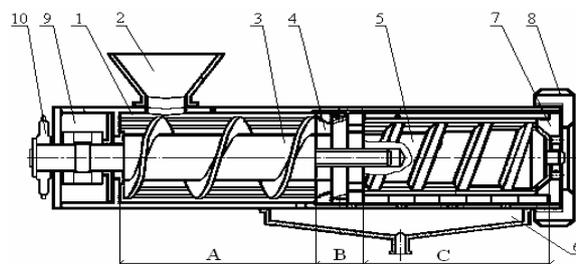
Схема процессов измельчения и прессования мясокостной шквары в экспериментальной установке: А - зона транспортирования, В - зона измельчения, С - зона прессования; 1 - цилиндрический корпус; 2 - бункер; 3 - транспортирующий шнек; 4 - режущий механизм; 5 - прессующий шнек; 6 - поддон для сбора жидкой фракции; 7 - регулируемая диафрагменная конусная решетка; 8 - зажимная гайка; 9 - подшипниковая опора; 10 - звездочка
